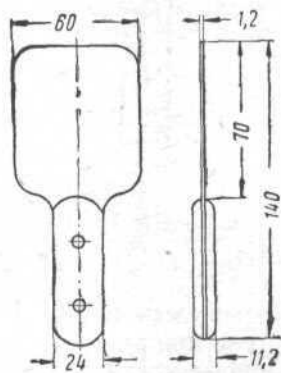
Лопатка для заправки боковой кромки обивки потолка
